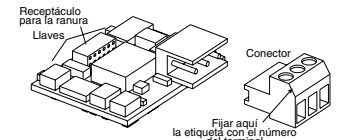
Desenchufe el conector antes de instalar el módulo.
